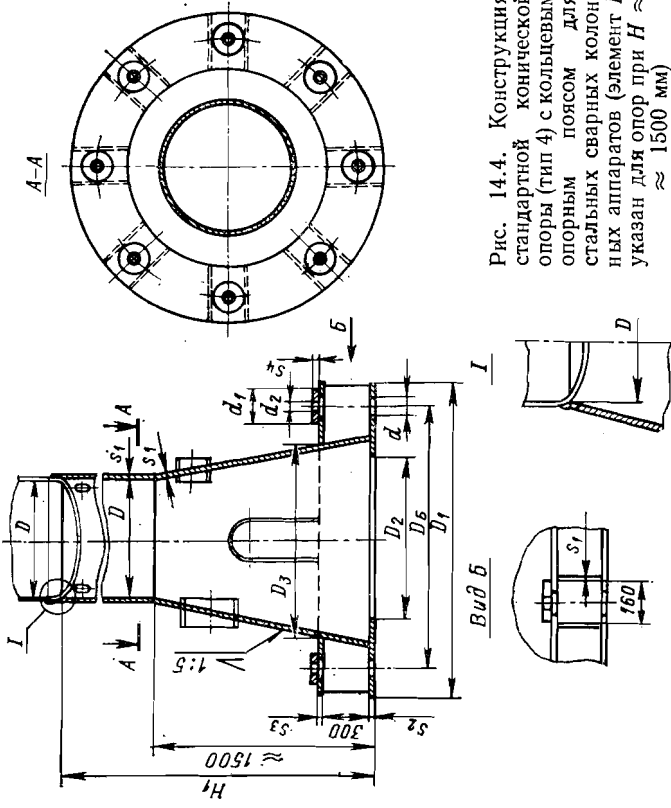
Конструкция стандартной конической опоры (тип 4) с кольцевым опорным поясом для стальных сварных колонных аппаратов (элемент I указан для опор при H ≈ 1500 мм)
